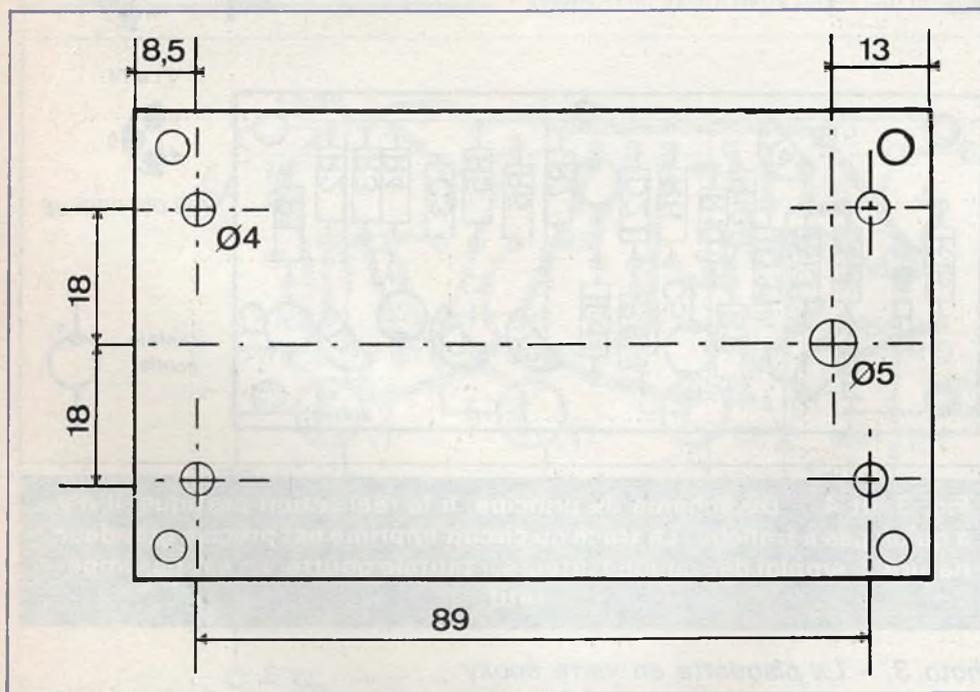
Le montage pourra facilement se loger à l'intérieur d'un coffret P/2 dont la face avant subira le plan de perçage ci-dessus.
